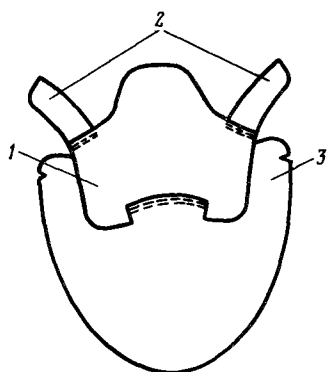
Схема соединения полуглухого клапана 1 с подблочниками 2 и союзкой 3 в заготовках полусапог-сверхом из юфти
